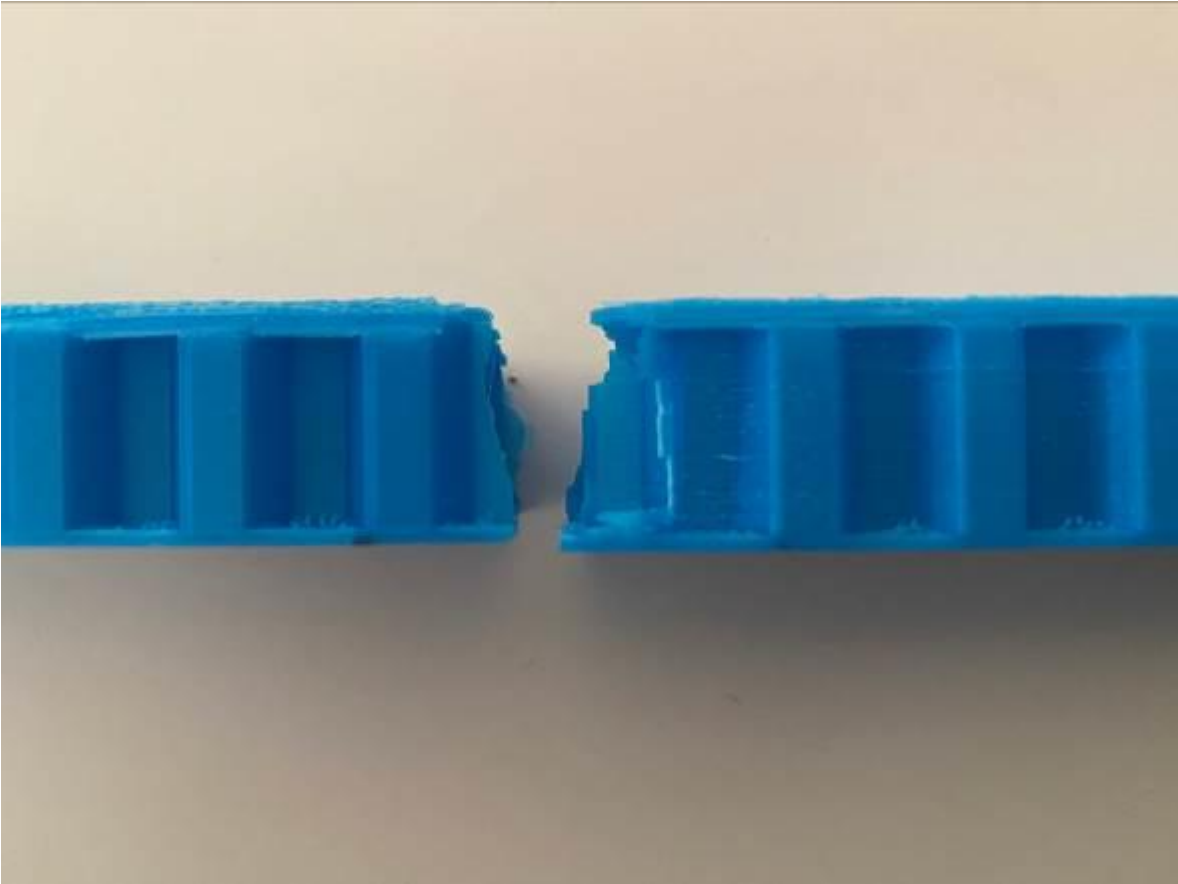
Espécimen 3 del lote de 1/4" fabricado completamente en PLA; tipo de falla X-A-F.
